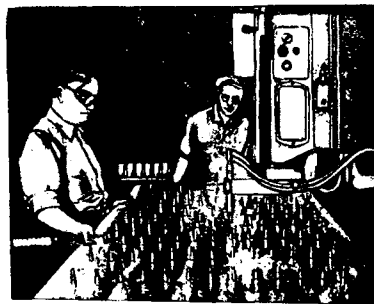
Сварка нервюры из дуралюминовых деталей на сварочной машине высокой мощности
